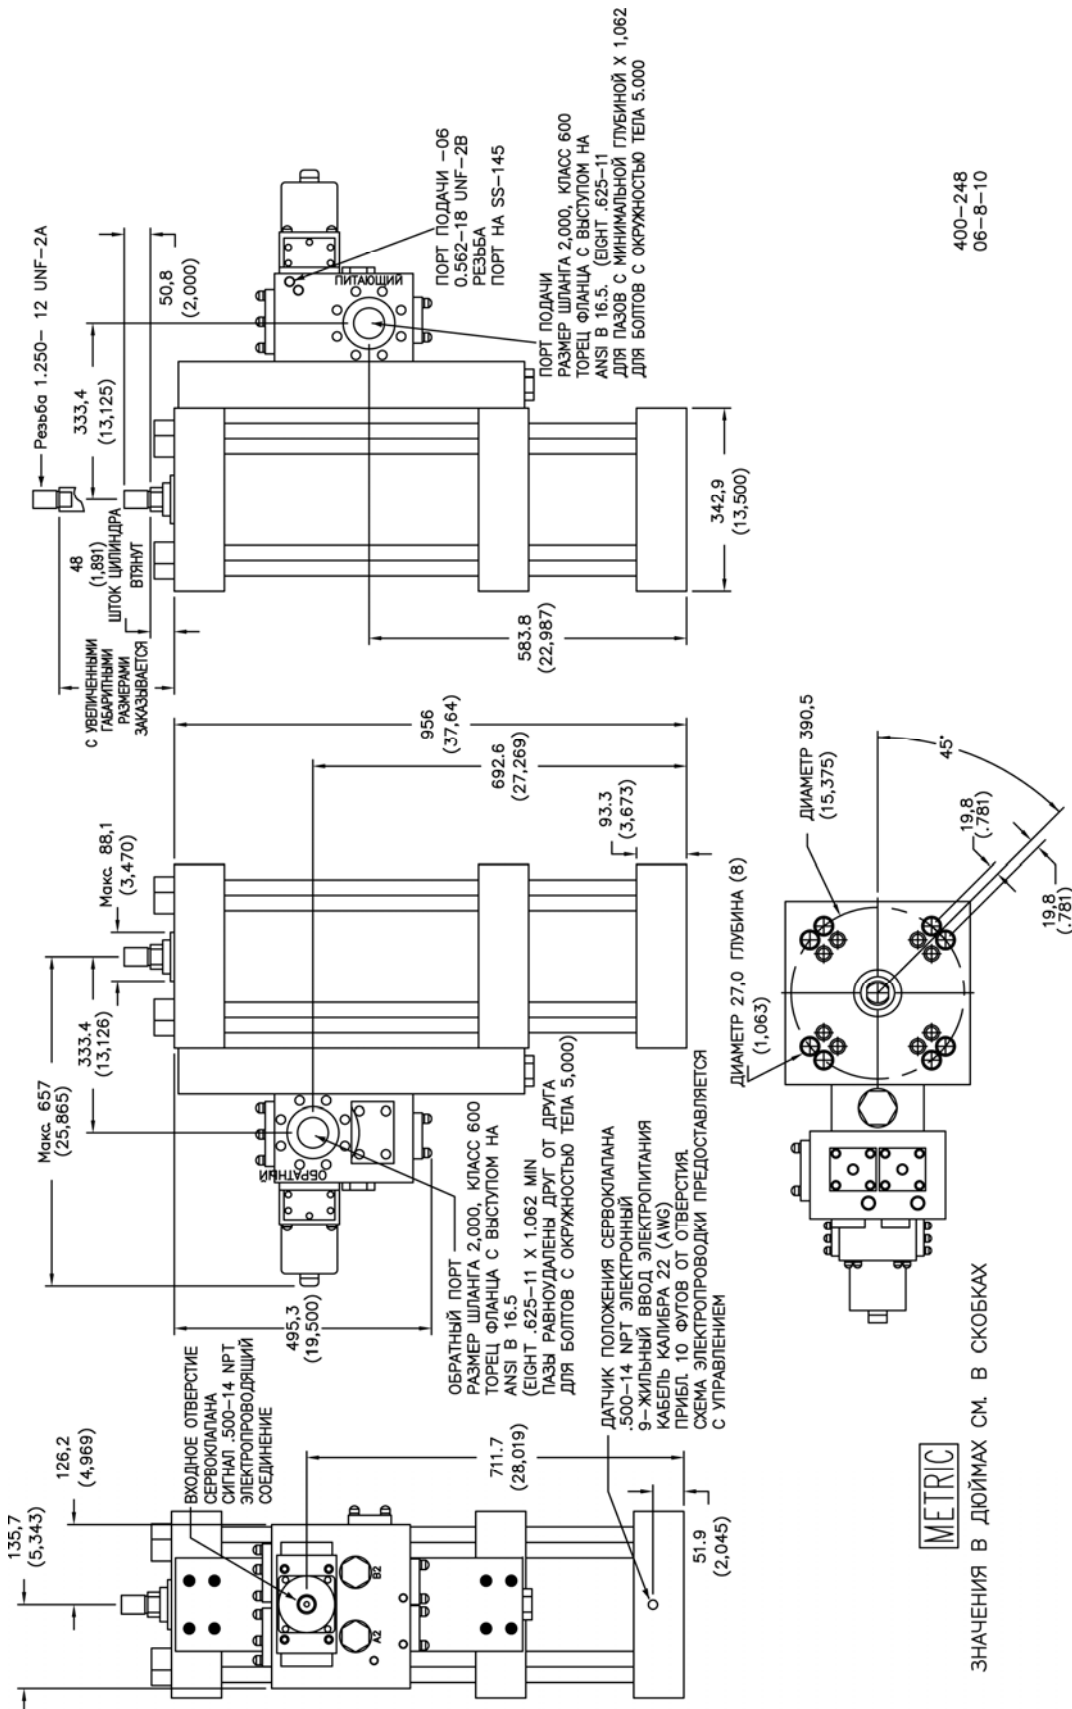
Габаритный чертеж электрогидравлического исполнительного цилиндра
